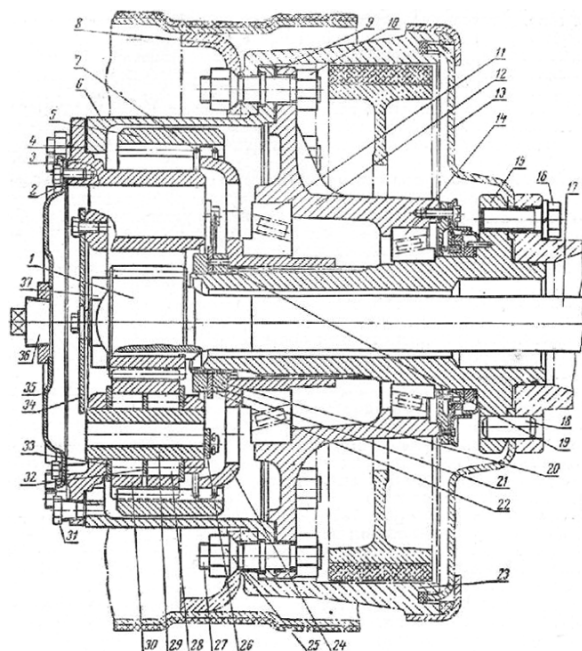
Загальний вигляд планетарного редуктора колісного трактора Т-150К [5]
